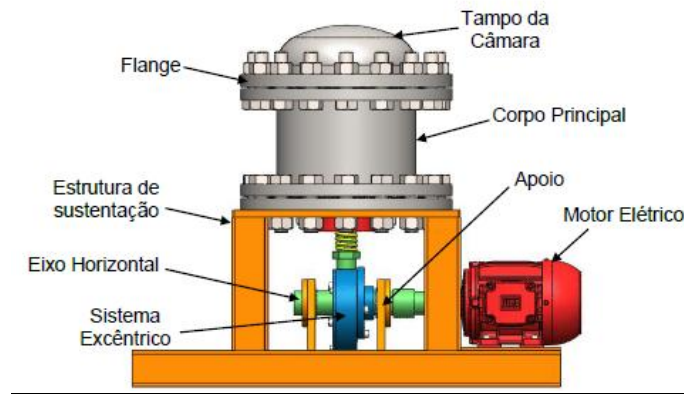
Vista Frontal da Máquina de Ensaios de Corrosão-Fadiga com a indicação de componentes
